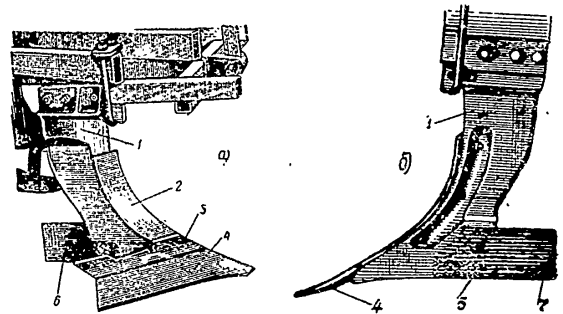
Рабочий корпус для безотвальной пахоты: а — передний корпус; б — задний корпус; 1 — стойка; 2 — щиток; 3 — уширитель; 4 — лемех; 5 — полевая доска задняя; 6 — полевая доска передняя; 7 — плетка
